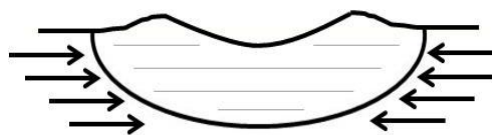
La compresión se opone a la fisuración [49]
